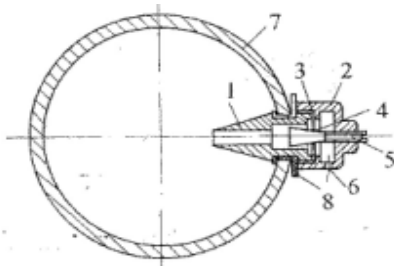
Капельница с мембраной с центральным отверстием (1- корпус; 2-крышка; 3-упругая резиновая мембрана; 4-центральное отверстие; 5- подвижный шток; 6- водовыпускное отверстие; 7- поливной трубопровод; 8- манжет.
